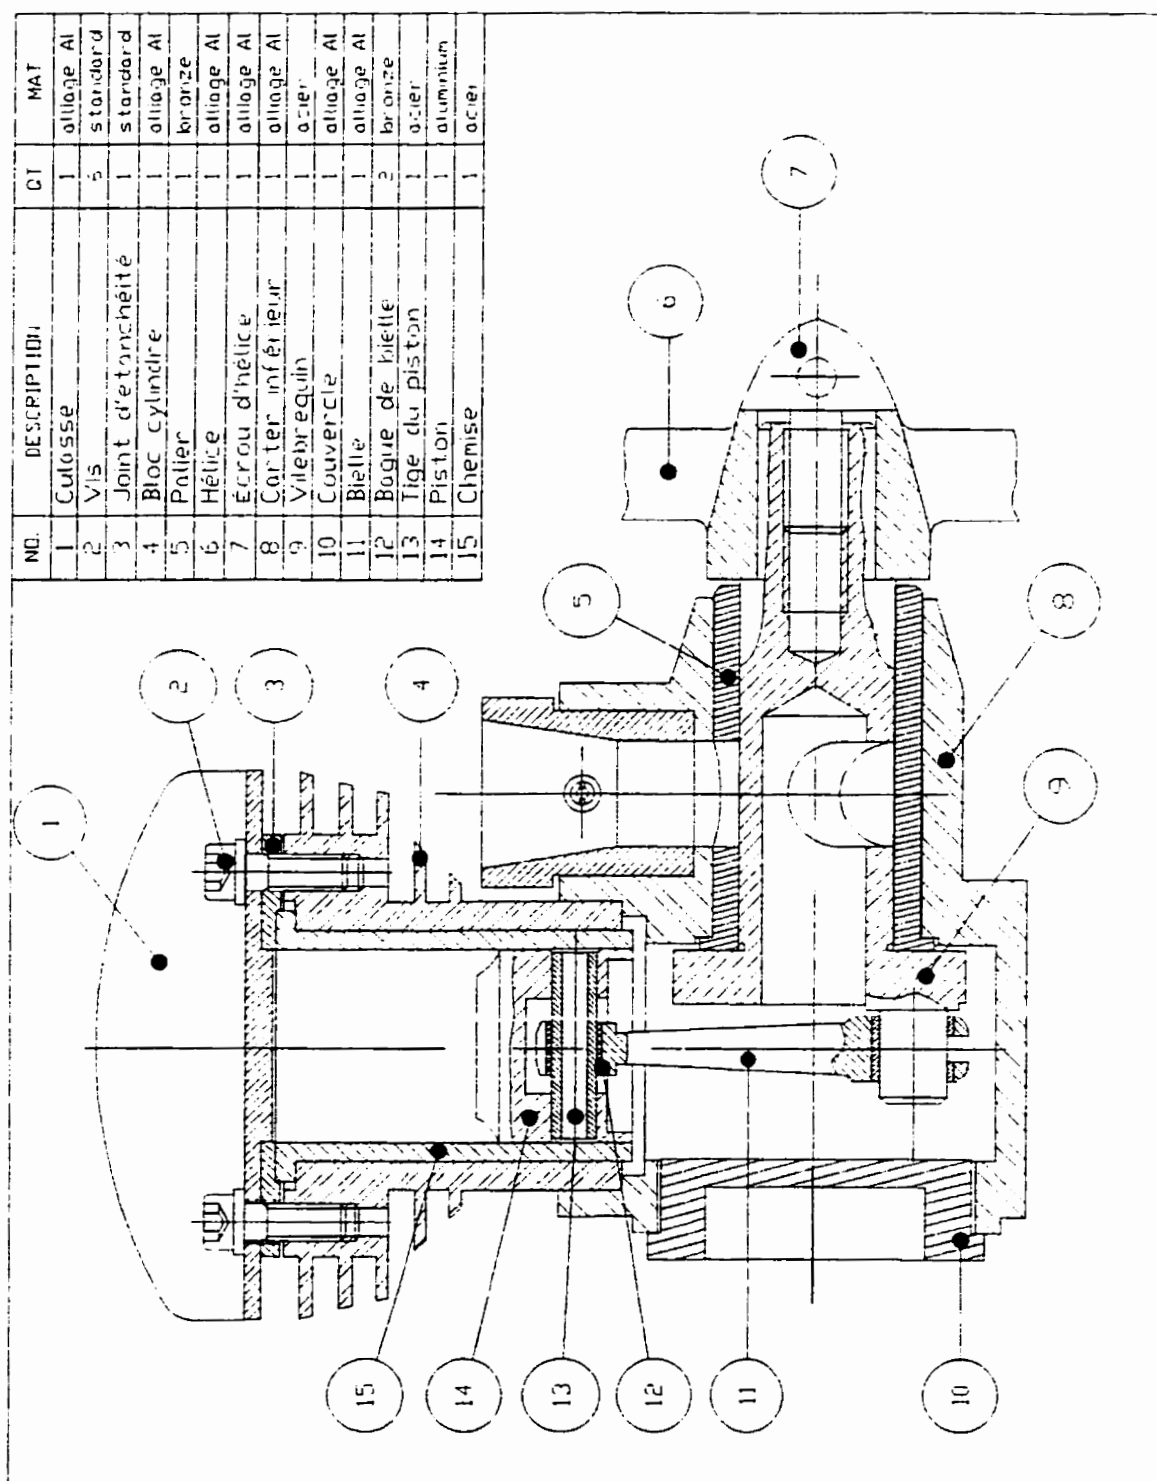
Dessin d'ensemble d'un moteur à explosion 2 temps
